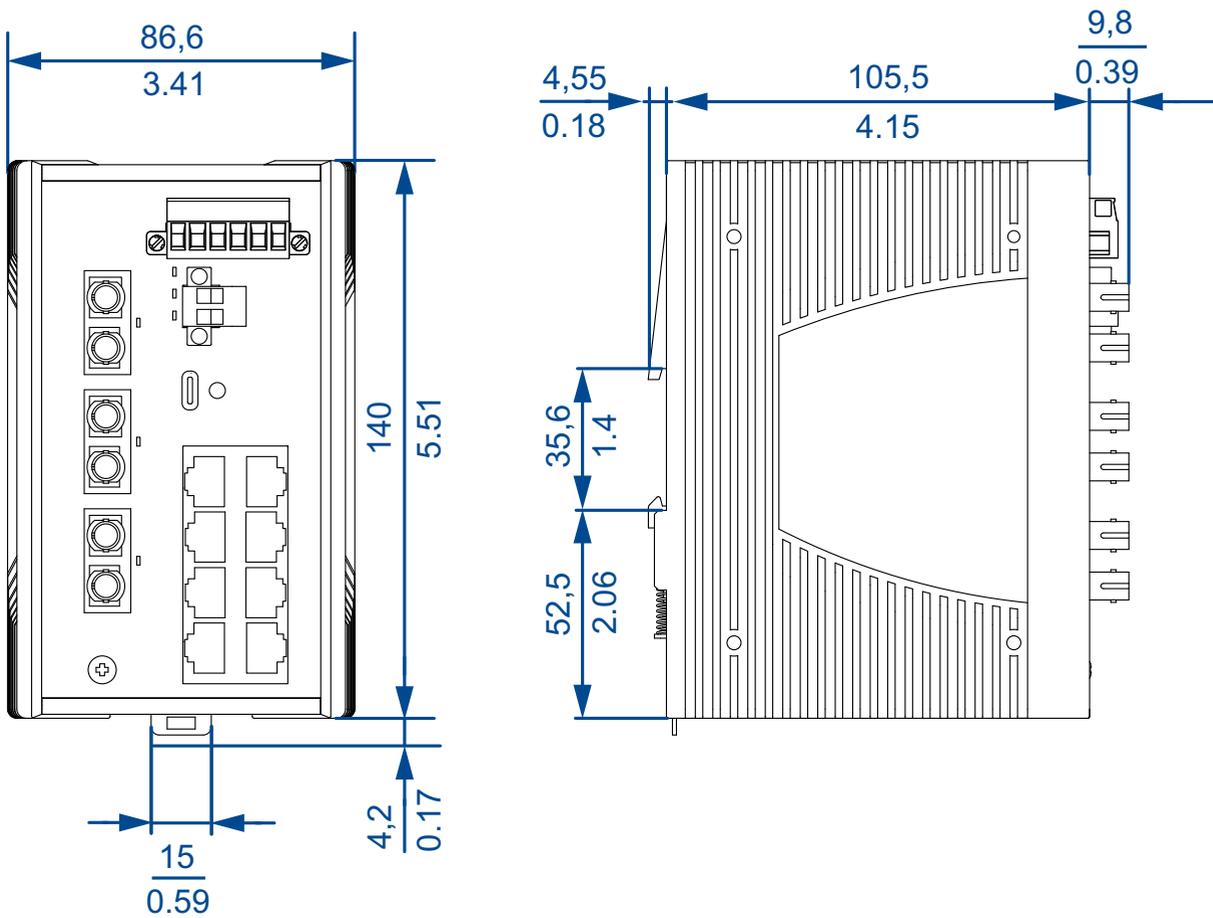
Gerätevarianten im mittleren Metallgehäuse
